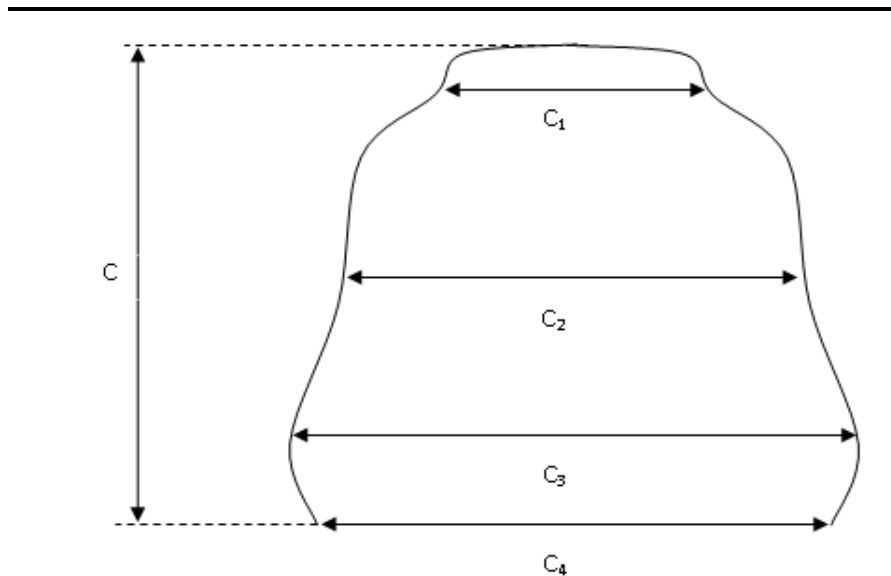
Mesure des dimensions de capot de l'isolateur
